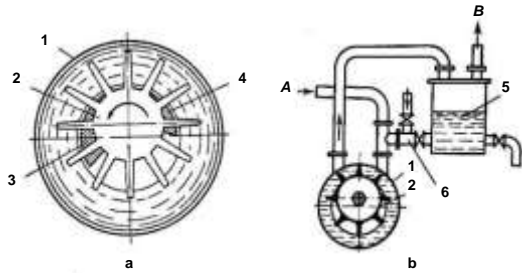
Схема ротаційного водокільцевого компресора (а) і схема його розміщення для відкачування газів (б): 1 – корпус; 2 – ротор; 3 – всмоктувальний отвір; 4 – нагнітаючий отвір; 5 – бак; 6 – переливна труба для заповнення вакуумнасоса рідиною; А – відкачуваний газ; В – вода
